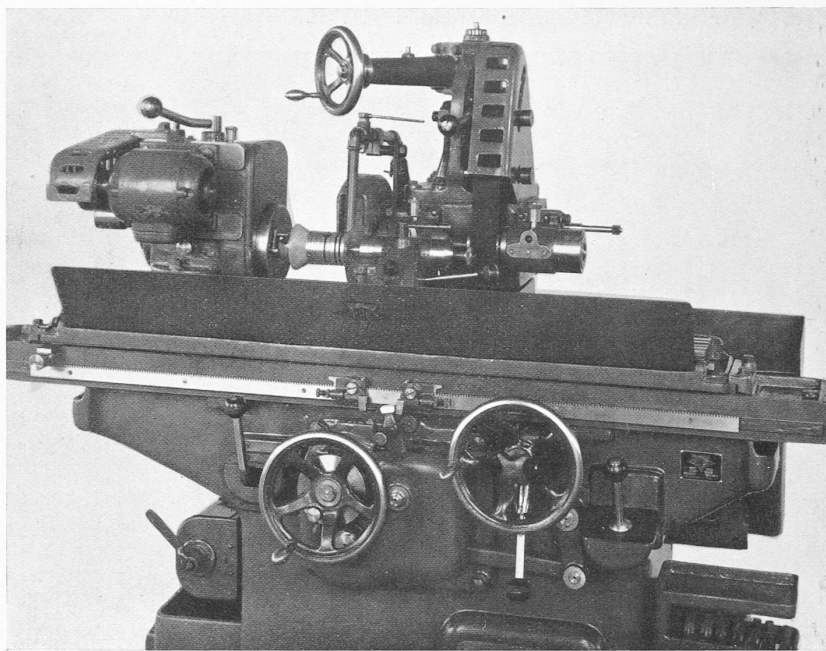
Kombinierte Rund-, Innen- und Planschleifmaschine (Kellenberger Werkzeugmaschinenfabrik).
